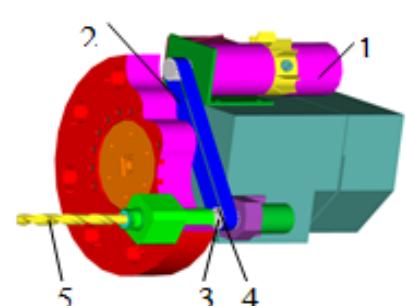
Схема шестипозиционной револьверной головки с вращающимся инструментом: 1 – приводной двигатель; 2 – зубчатая ременная передача; 3, 4 – полумуфты; 5 – инструмент
